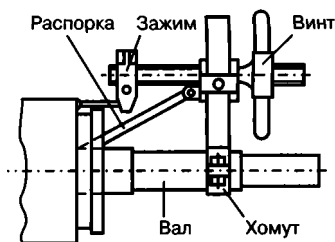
Приспособление для извлечения стержней из пазов ротора
